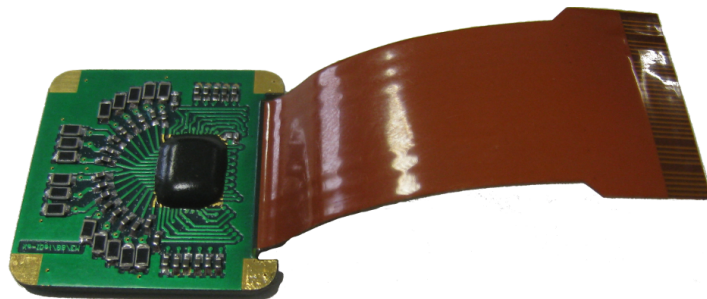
Vue de l'électronique frontale IDeF-X.
